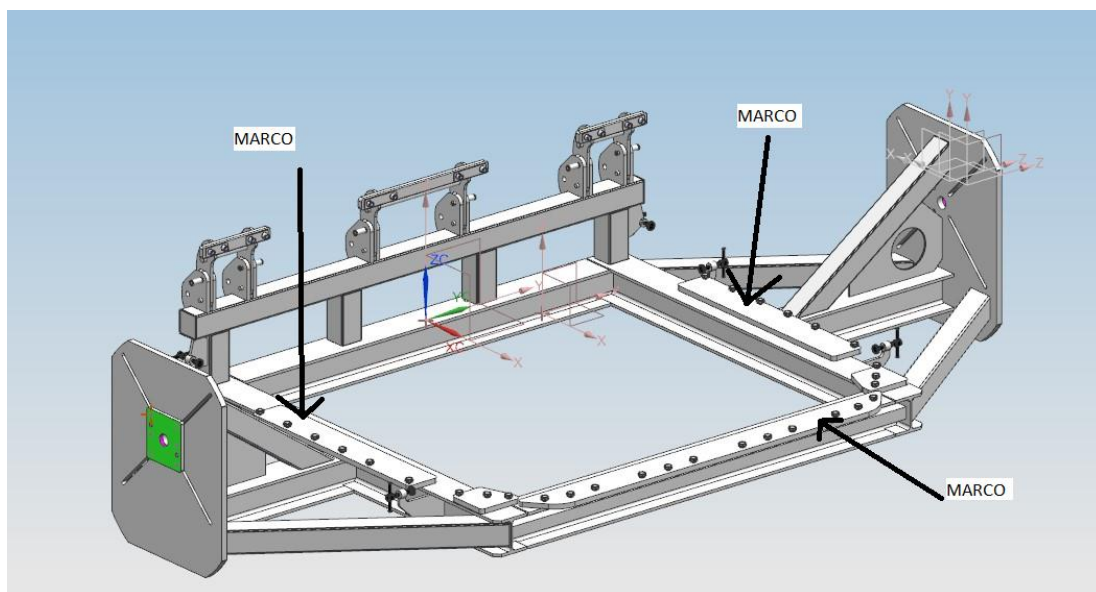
Estructura desnuda del Útil de soldar cabina con código U17053400S001100
